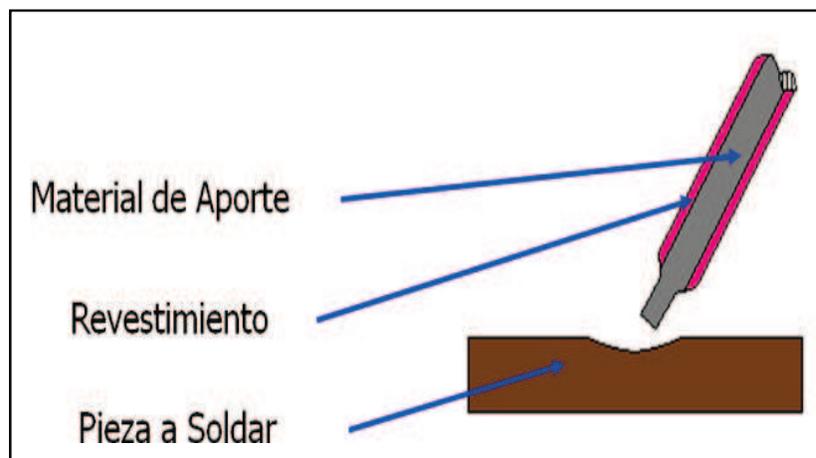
Proceso de Soldadura SMAW.
